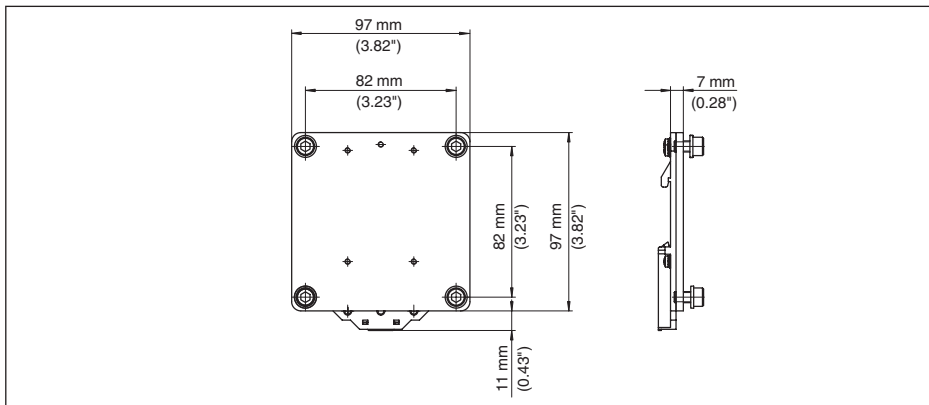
Placa adaptadora para montagem do VEGADIS 82 em trilho
